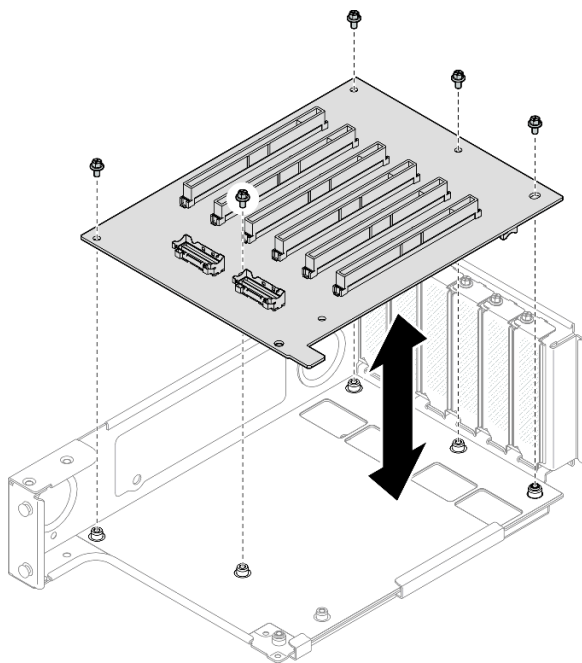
Removendo o cartão da placa riser PCIe da placa riser
